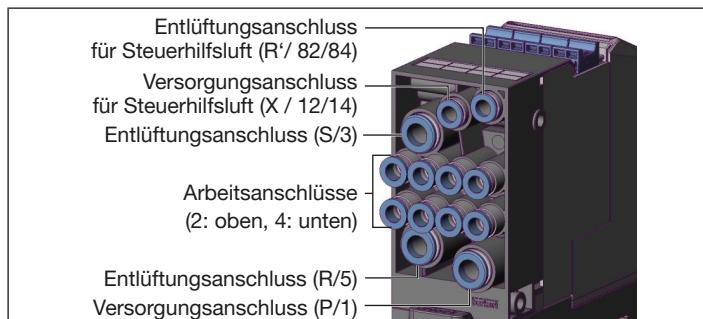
Belegung der pneumatischen Anschlüsse am Feldmodul
